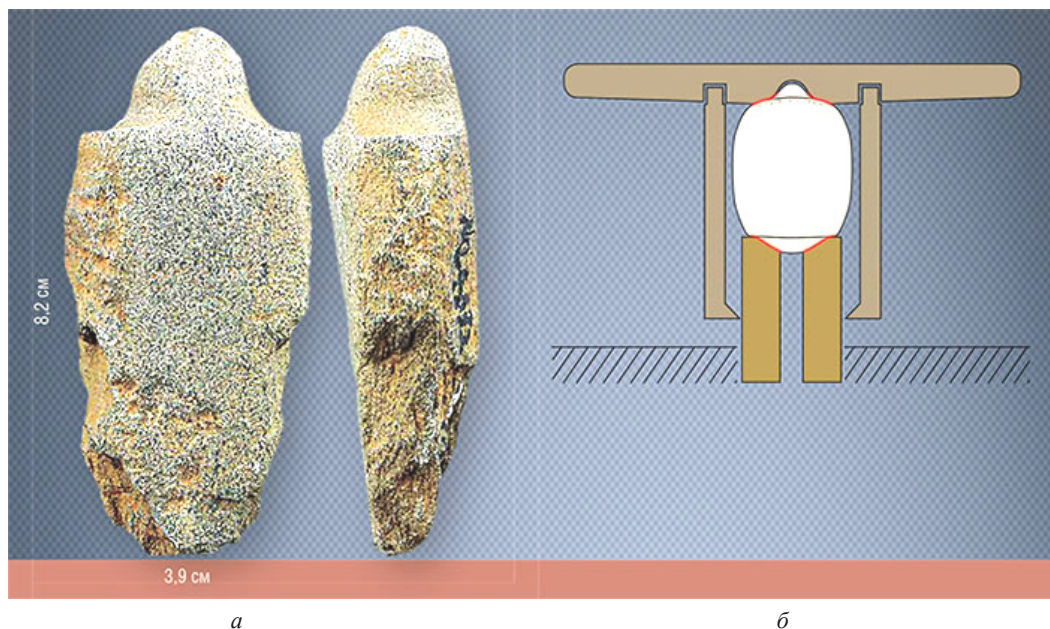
Схема установки каменного подшипника (а) в основании вращающегося стола древнего сверлильно-фрезерного станка (б) («восточная» технология)¹
